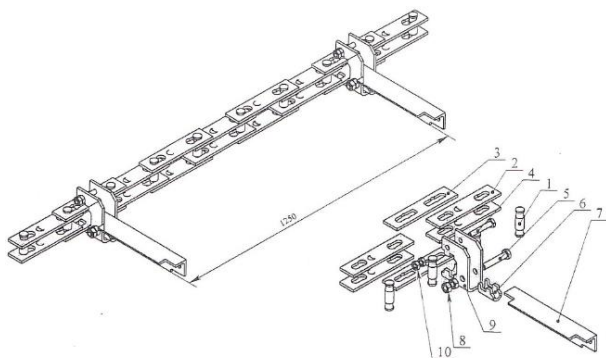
Рабочий орган транспортера ТСН-2.0Б: 1 – ось; 2 – планка; 3 – планка скобы; 4 – болт М10х60; 5 – болт М12х65; 6 – скоба; 7 – скребок; 8 – гайка М12; 9 – скоба; 10 – гайка М10.
